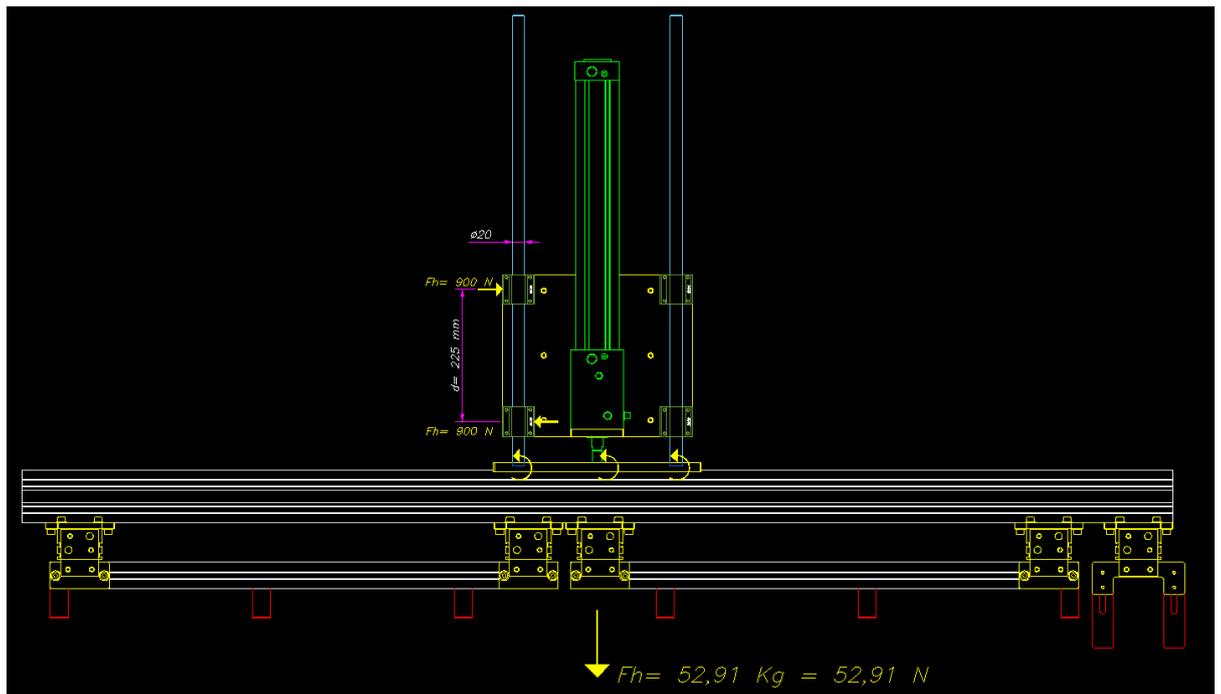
Cargas a tener en cuenta para el dimensionado del pistón neumático
